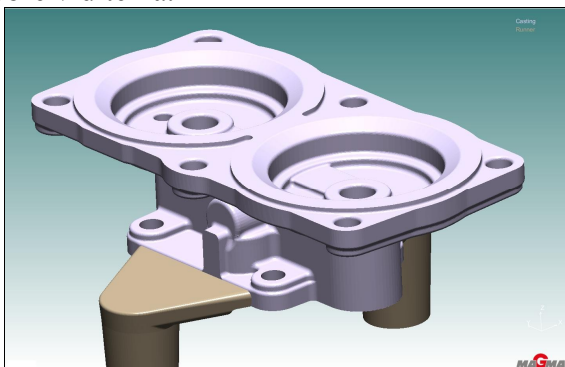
Původní design odlitku včetně vtokové soustavy pro vysokotlaké odlévání
